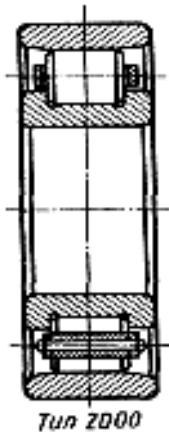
Роликовый радиальный подшипник с короткими цилиндрическими роликами
